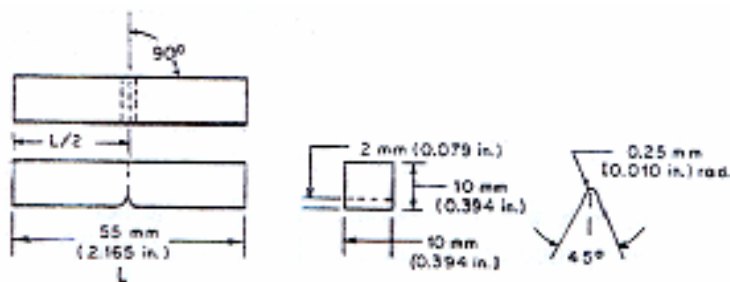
Corpo de prova de impacto com dimensões padrões, usinado conforme designação A370[43].
